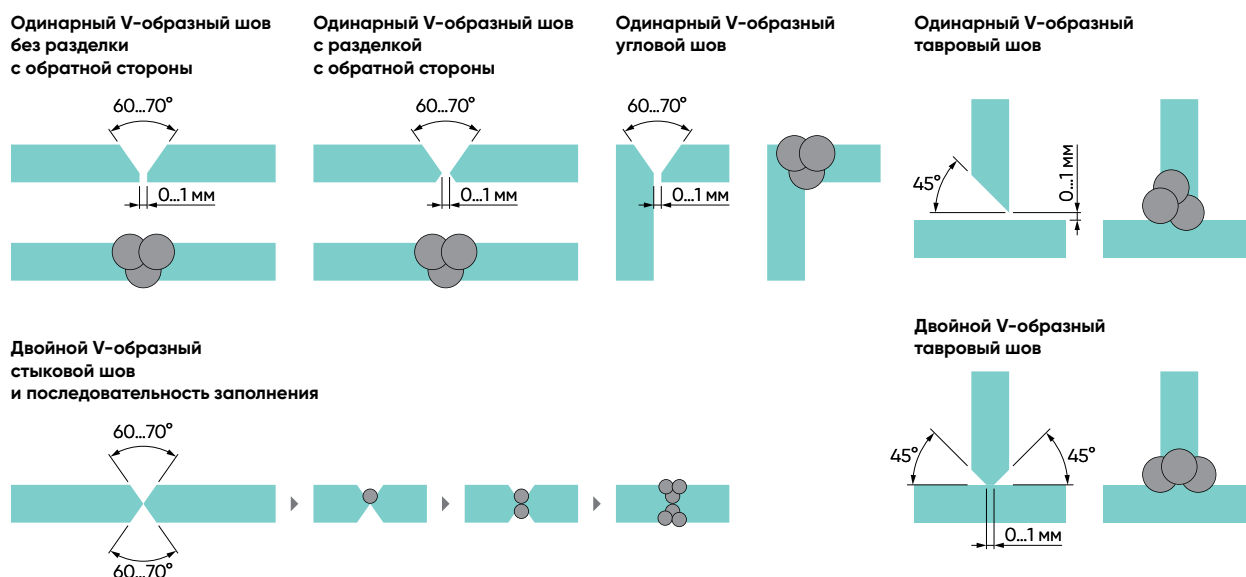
Разделка сварочных кантов при сварке листовых материалов
